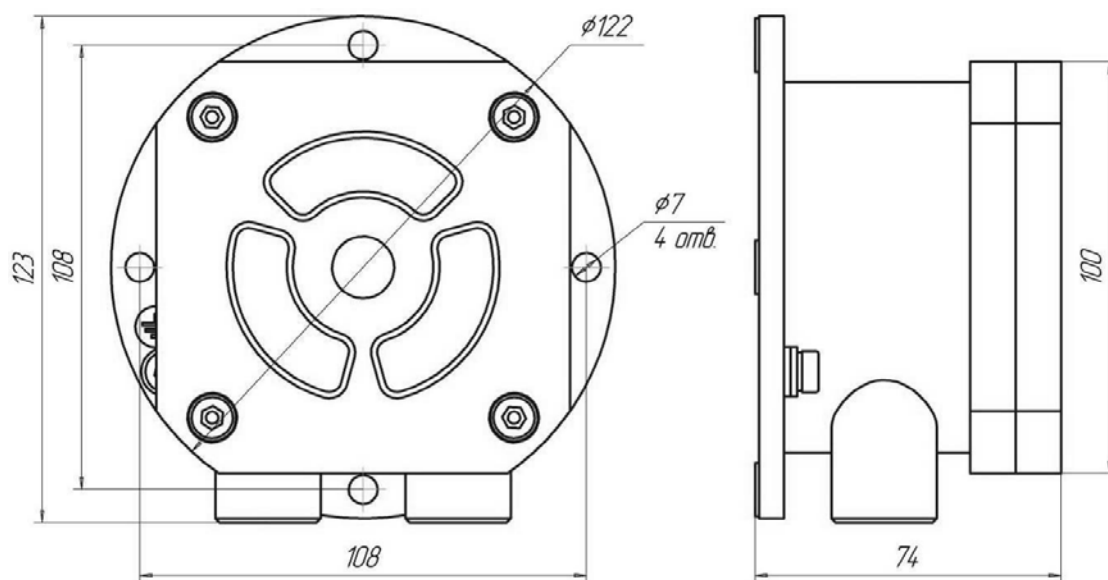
Оповещатель пожарный взрывозащищенный комбинированный
